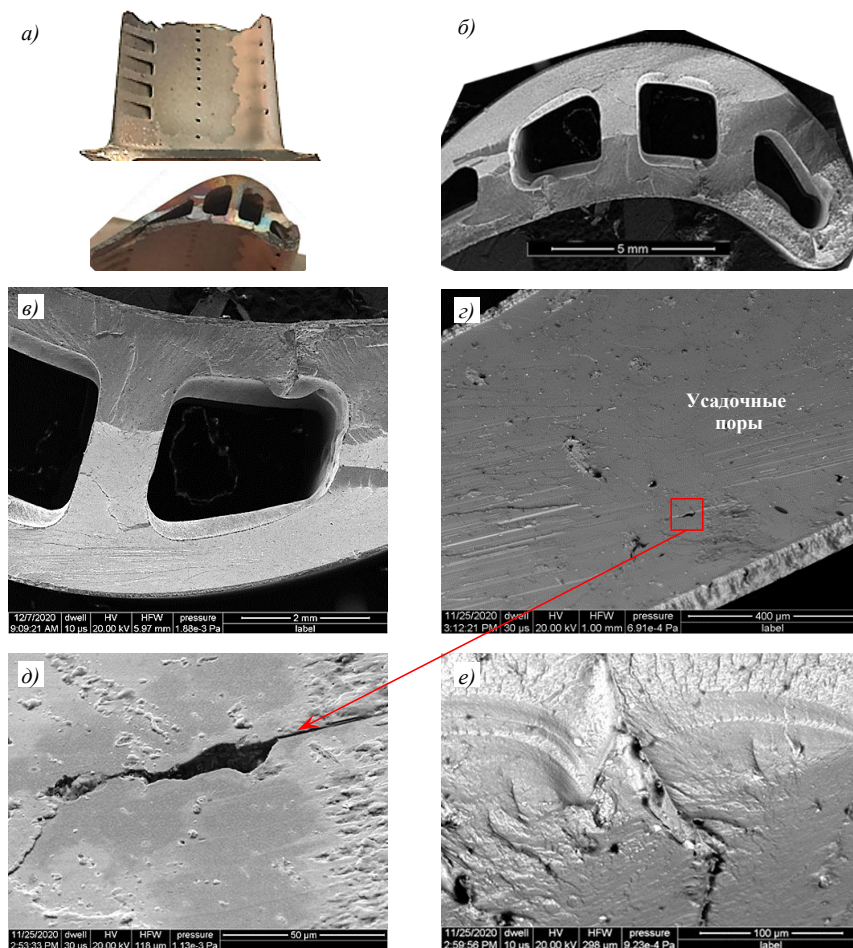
Строение излома лопатки 2 из сплава ЖС26-ВИ после наработки 1600 ч: *a* – общий вид разрушенной лопатки; *б, в* – общий вид излома; *г, д* – пора в очаговой зоне; *е* – зона перехода усталостного разрушения к долому
